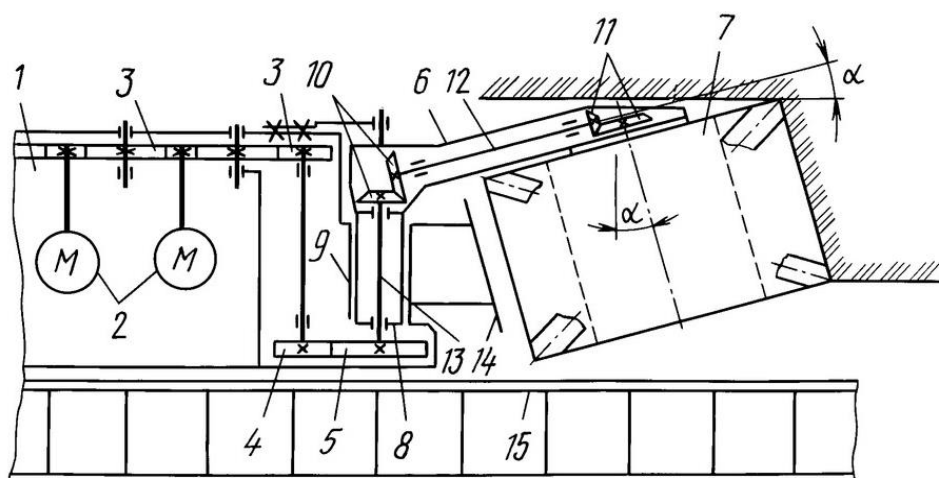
Общий вид очистного комбайна с противоположным размещением рукояти поворотного редуктора резания с установленным под углом к массиву исполнительным органом
